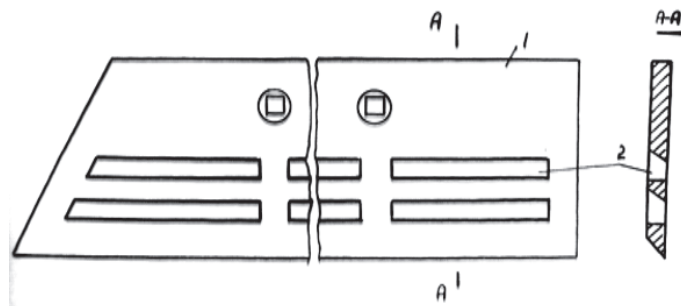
Почвообрабатывающий рабочий орган Н.П. Заватскоо, И.Г. Шульгина (ОКБ ЦелинНИИМЭСХ)
